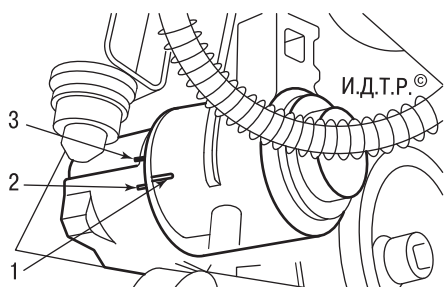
Метки на корпусе автоматического натяжителя: 1 – метка на подвижном рычаге натяжителя; 2, 3 – метки на корпусе натяжителя
